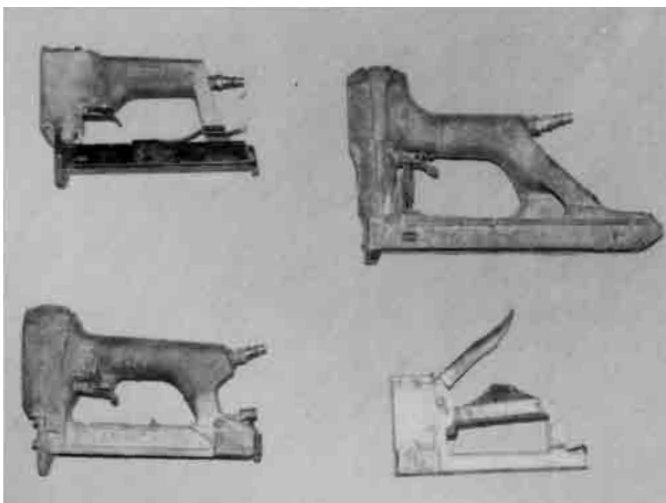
Klammer-Pistolen und Tacker (Fabr. Duo-Fast). Im Uhrzeigersinn: Druckluft-Klammerpistole; Druckluft-Tacker, schwere Ausführung; Hand-Tacker; Druckluft-Tacker, leichte Ausführung.
